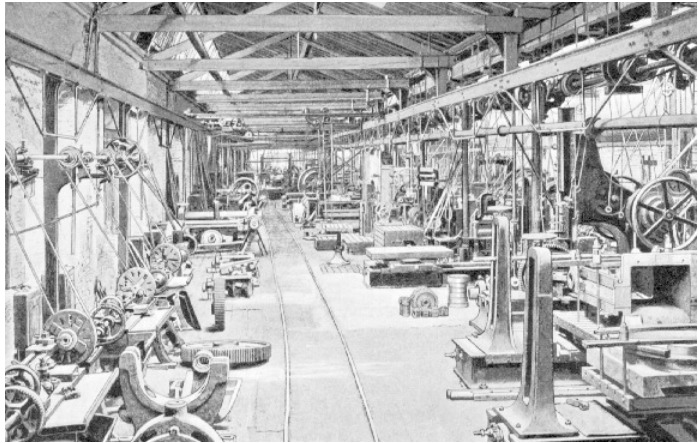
Dreherei der Werkzeugmaschinenfabrik Schieß in Düsseldorf
